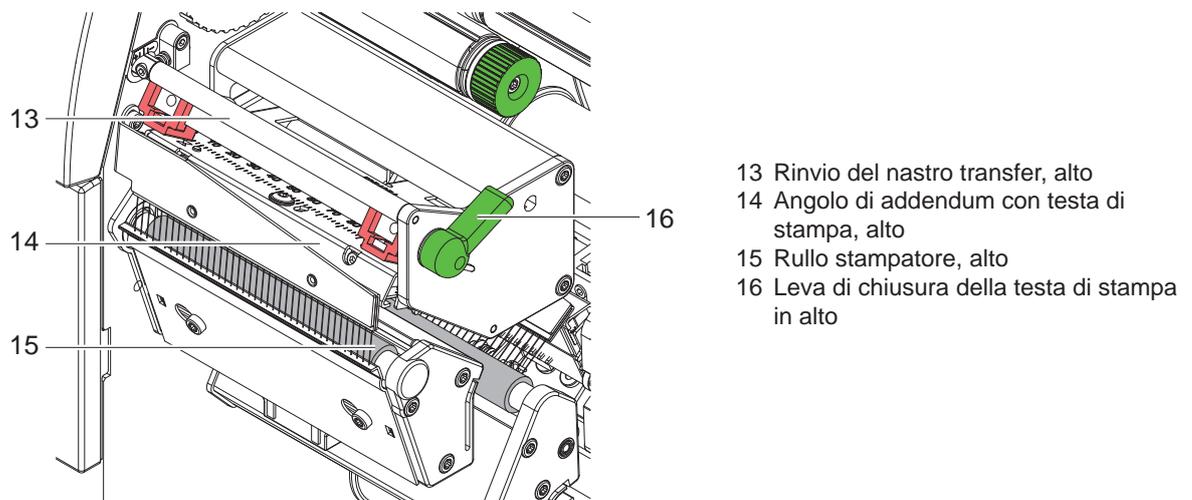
Meccanica di stampa – gruppo stampante superiore per la stampa del colore principale
